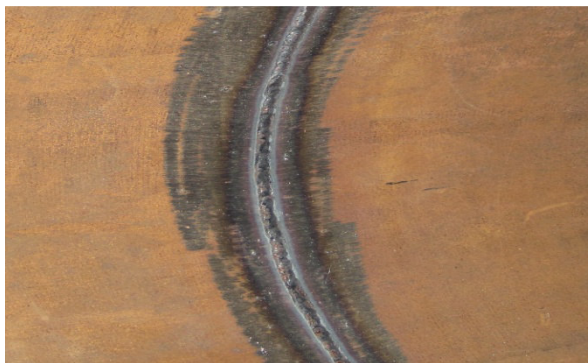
Обратный валик шва при сварке металлопорошковой проволокой
